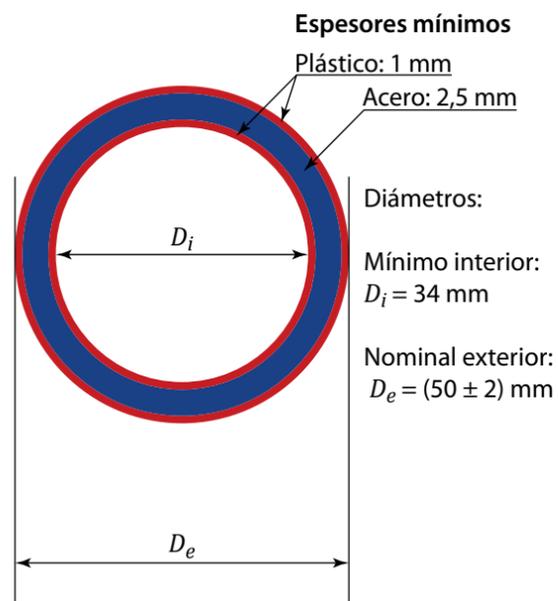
Caño aislado para pilar de conexión eléctrica domiciliaria (caño compuesto). Vista de la sección transversal (escala 1:1, aproximadamente). [Referencia: Norma IRAM 2477, esquema A2, octubre 2017]
